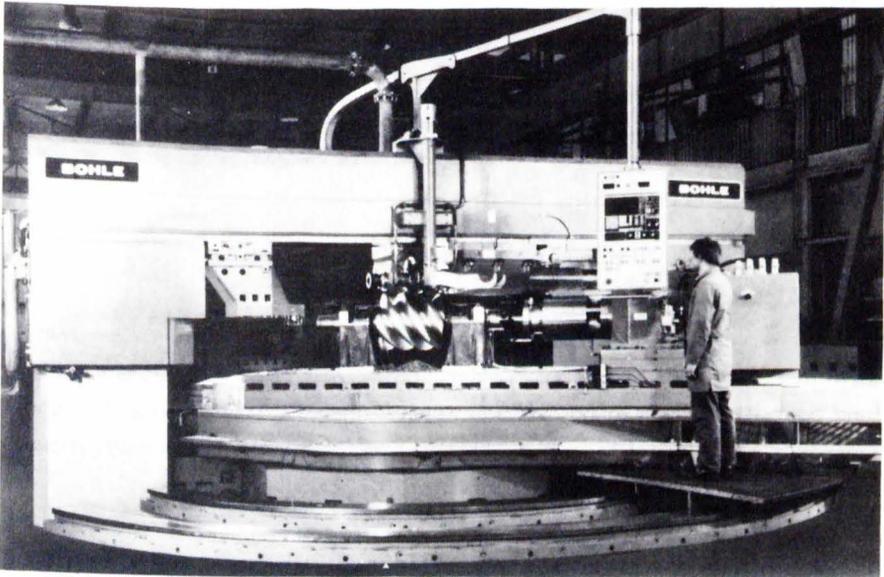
Rotorfräsmaschine Bohle FU P 200 NC.
